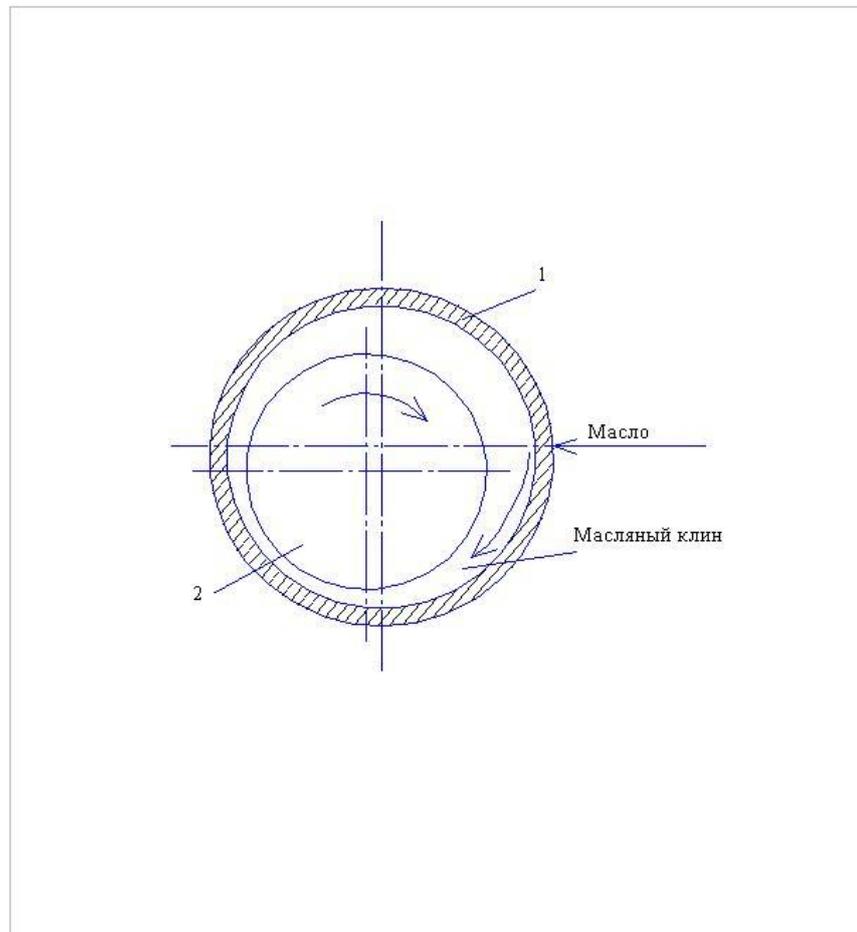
Схема гидродинамического ПЖТ: 1–втулка-вкладыш в подушке вала; 2–втулка-цапора на шейке вала.
